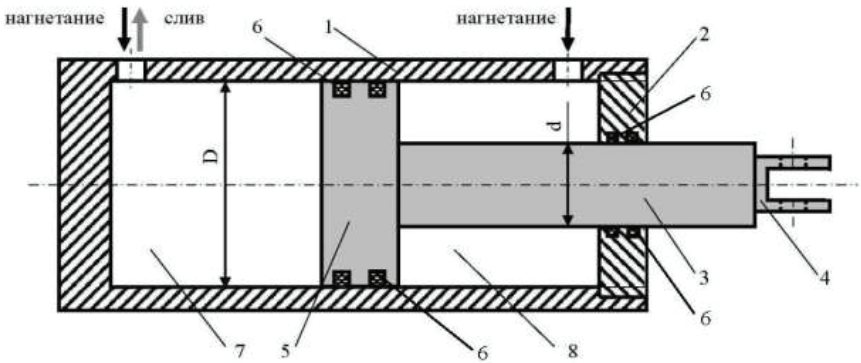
Схема дифференциального силового гидроцилиндра без ложного штока, где 1- корпус; 2- крышка; 3- шток; 4- проушина; 5- поршень; 6- уплотнительное кольцо; 7,8- полости гидроцилиндра
